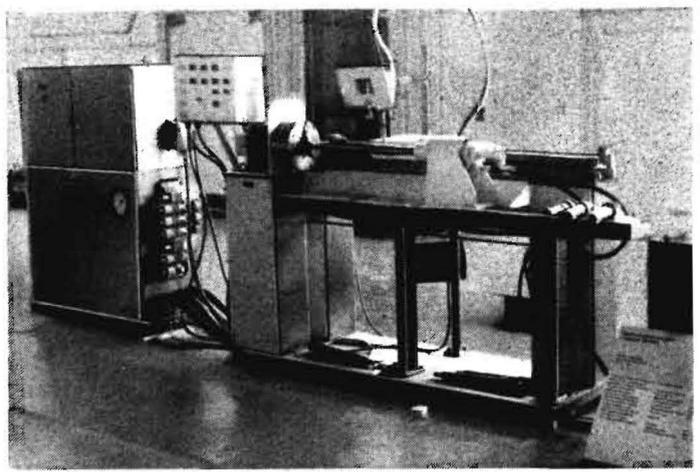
MAG-Auftragschweißroboter SR 05/K
